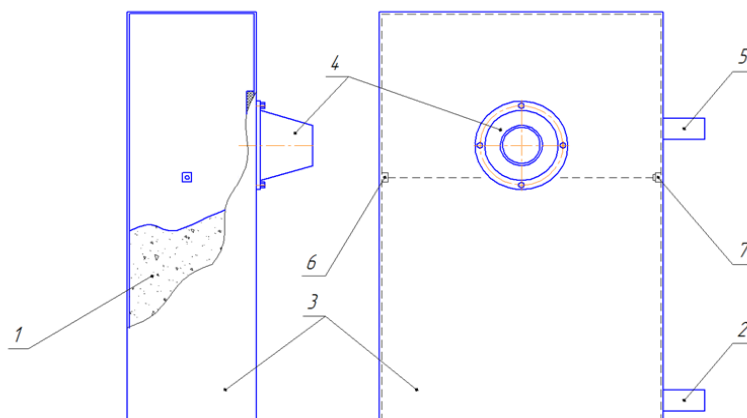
Схема бункера устройства для сбора свободного зерна с датчиком заполнения бункера: 1- зерно; 2- трубопровод для пневматической разгрузки; 3- корпус бункера; 4- конусная камера (камера разряжения); 5- трубопровод для поступления зерна; 6- приемник света; 7- источник света.
